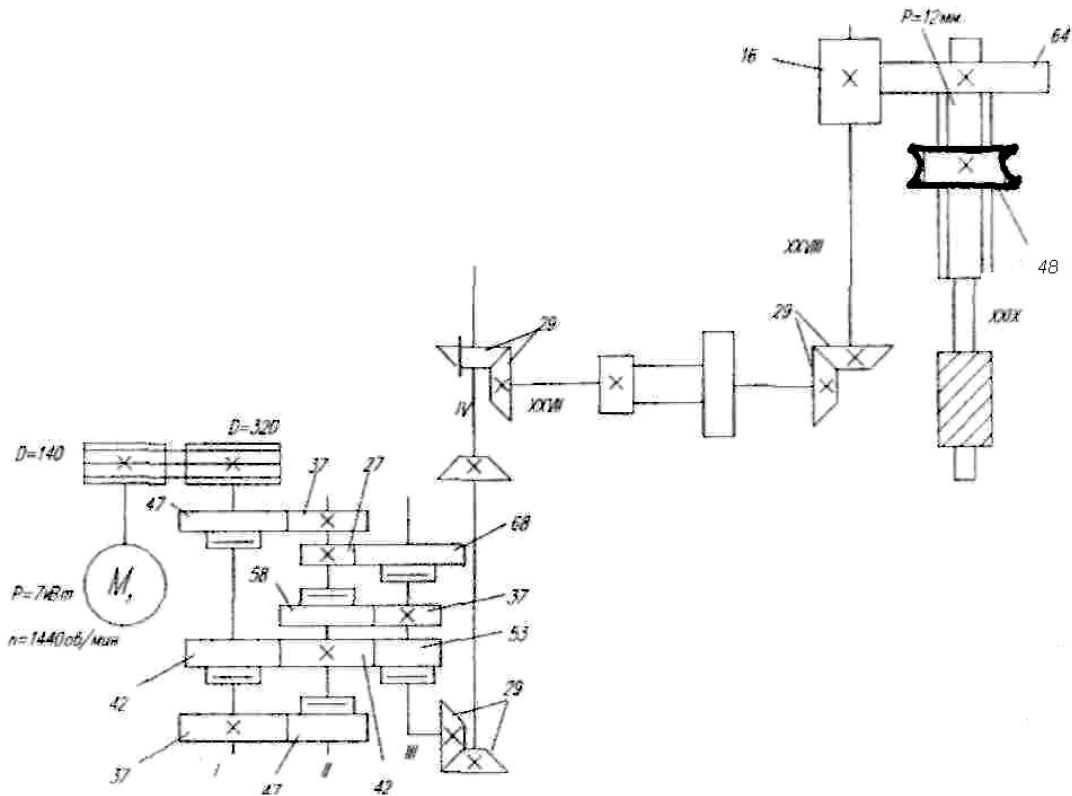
Кинематическая схема цепи главного движения станка 5К324
